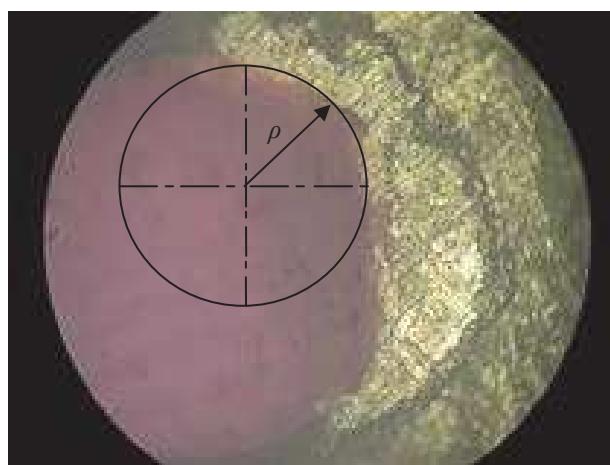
Фотография слепка режущей кромки ножа (400°C)
